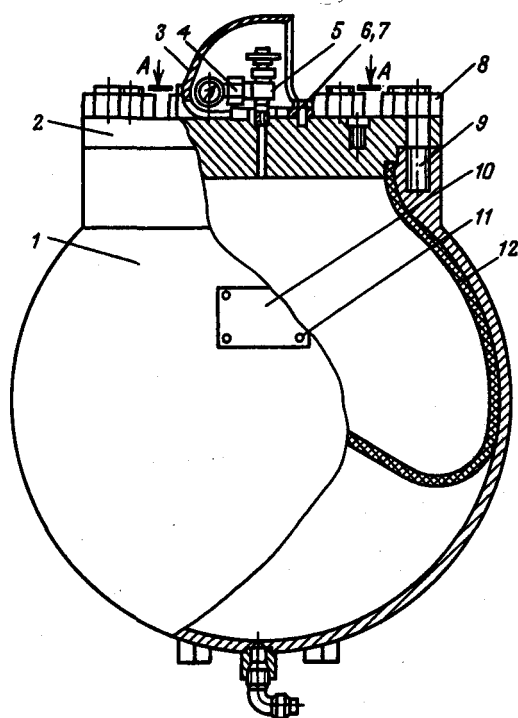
Пневмогидроаккумулятор гидроуправления превенторами ОАО "ВЗБТ": 1 – корпус; 2 – крышка; 3 – колпак; 4 – переходник; 5 – вентиль кислородный; 6 – болт; 7 – шайба; 8 – гайка; 9 – шпилька; 10 – табличка; 11 – заклепка; 12 – диафрагма разделительная
